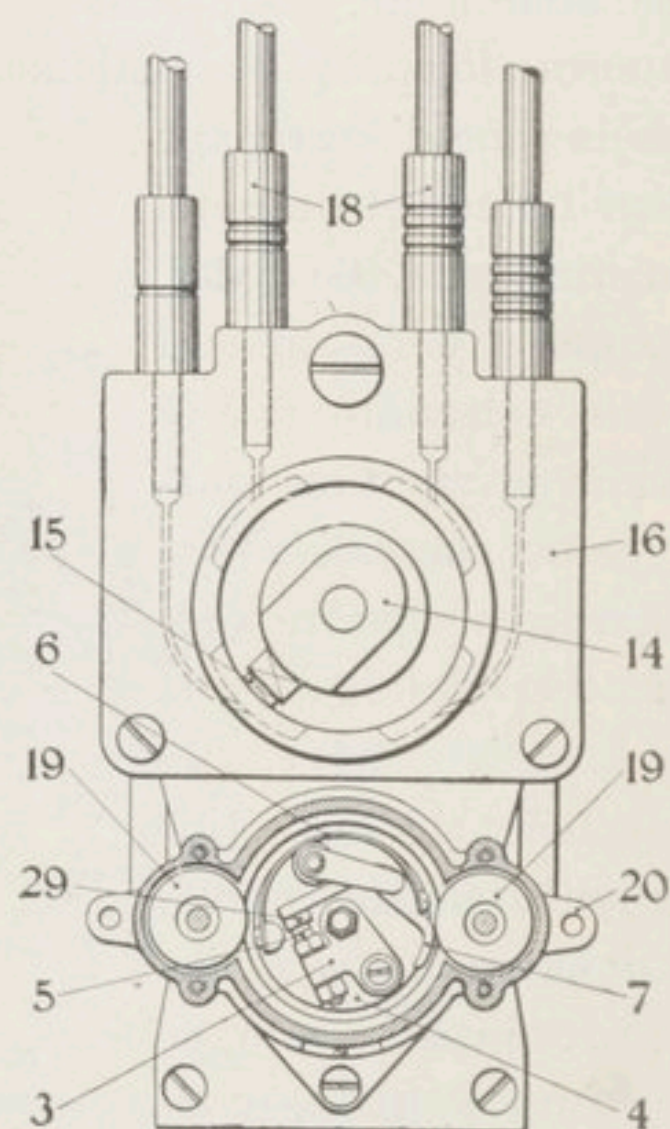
Magnéto Bosch pour moteur à quatre cylindres avec dispositif d'avance à l'allumage. Vue arrière.
